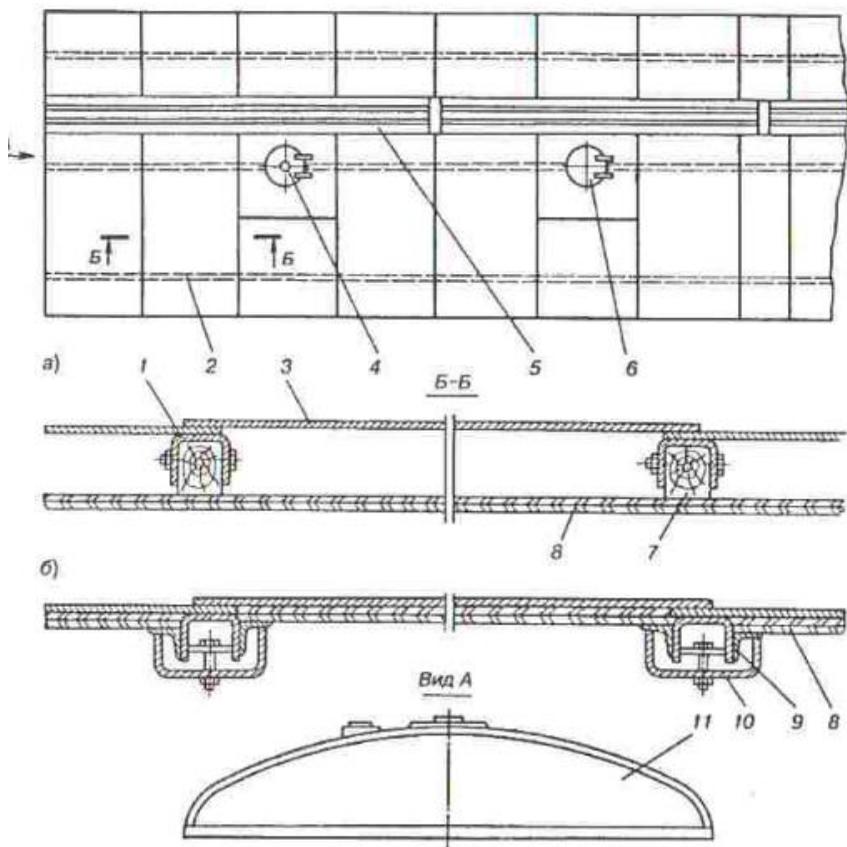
Крыша универсального крытого вагона со старым (а) и новым (б) способами укладки и крепления подшивки
